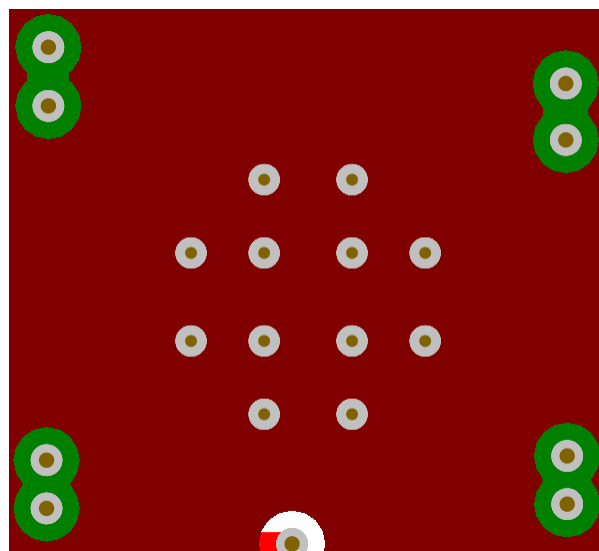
PCB Layout Example for LMK1D1212, GND Layer
